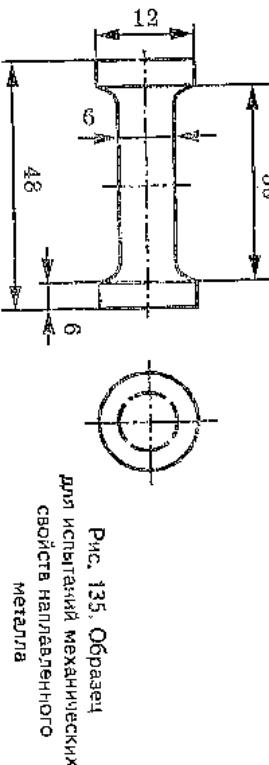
Образец для испытаний механических свойств наплавленного металла
